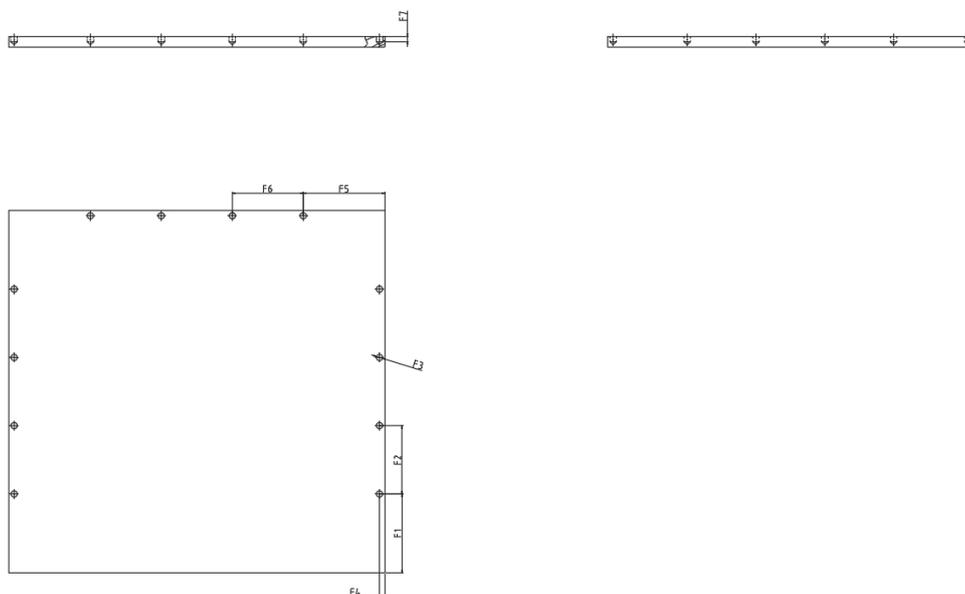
Plano Dimensionado Previo de la Base Cajón 2.1.5
